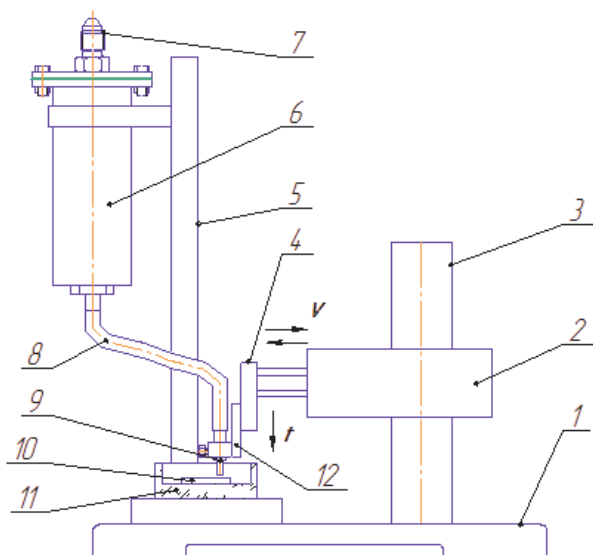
Схема экспериментальной установки для электрохимической струйной обработки: 1 — основание; 2 — приводной блок; 3 — стойка; 4 — каретка продольного хода; 5 — штатив; 6 — емкость для электролита; 7 — штуцер для подачи воздуха; 8 — шланг; 9 — катод-инструмент; 10 — деталь; 11 — электрохимическая ячейка; 12 — каретка вертикального перемещения
